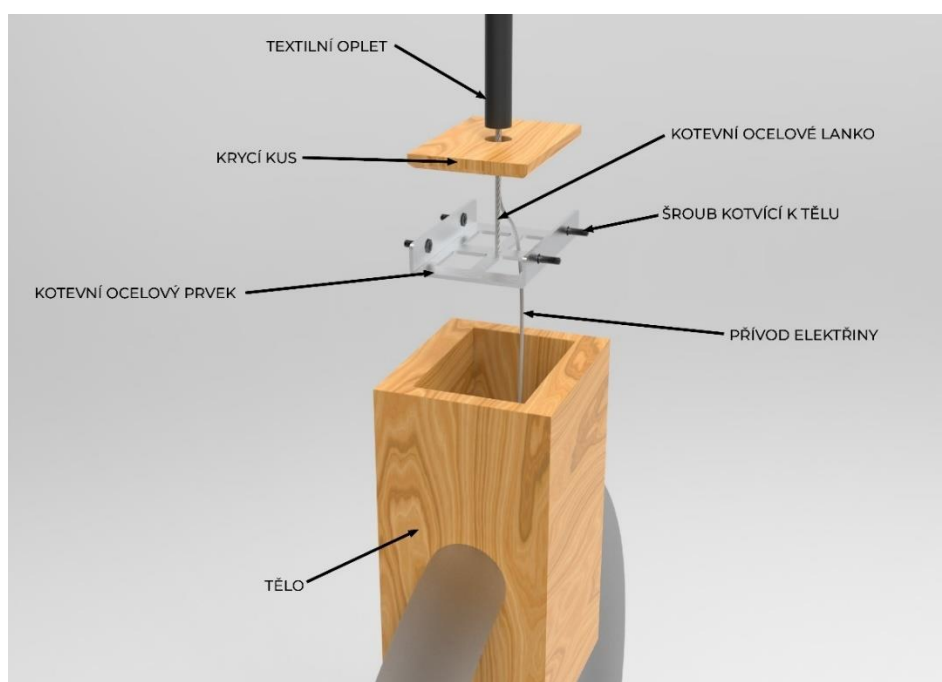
Vnitřní mechanismy a komponenty těla
